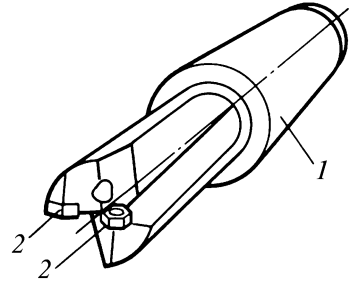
Сверло, оснащенное трехгранными твердосплавными режущими пластинами:
